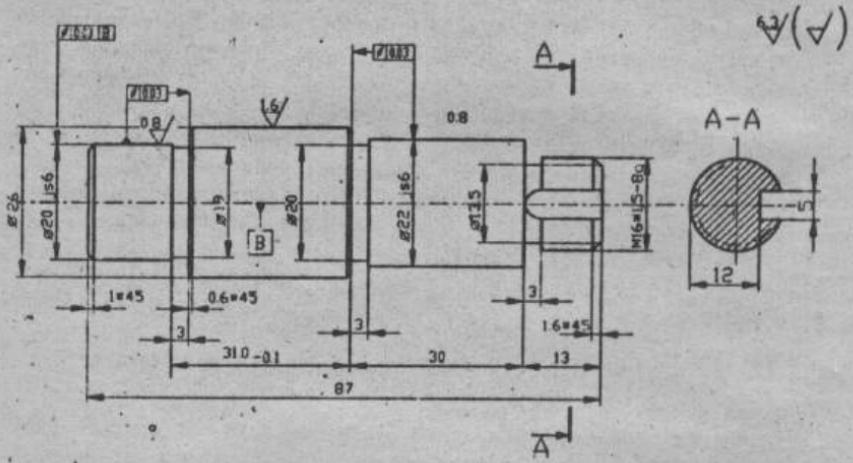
Вал (вид заготовки-прокат,матеріал-сталь 45,
